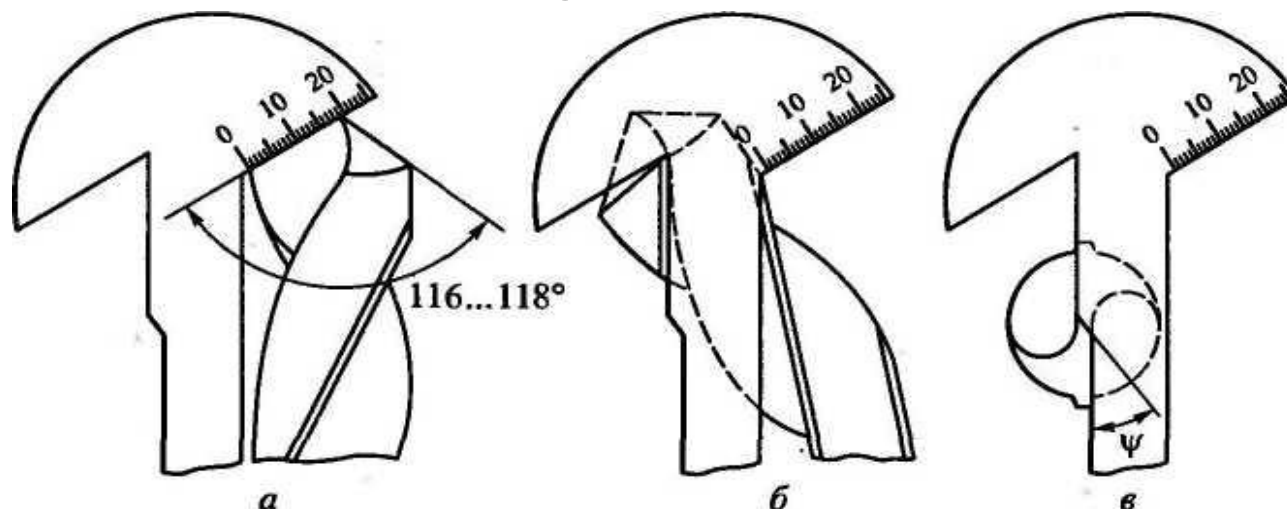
Шаблон для контроля заточки сверл: а - контроль угла при вершине; б - контроль угла наклона ленточки; в - контроль угла наклона поперечной режущей кромки; ψ - угол наклона поперечной режущей кромки
